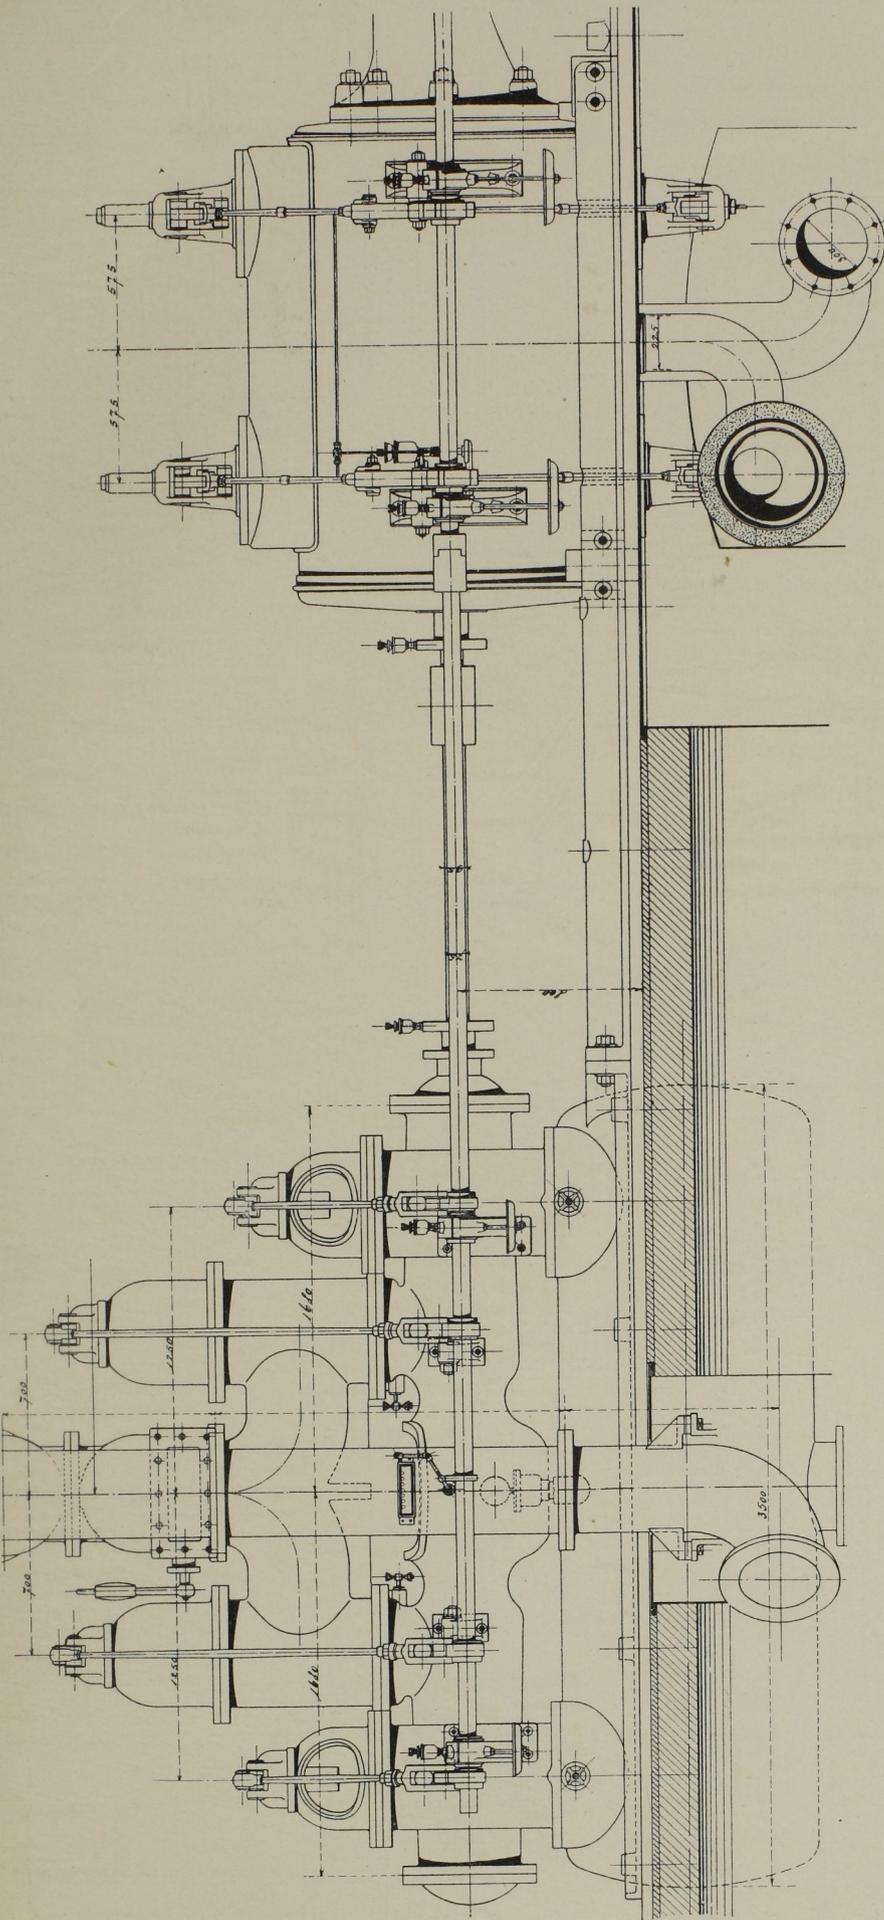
Seitenansicht der Pumpen und deren Steuerung. Massst. 1 : 30.
